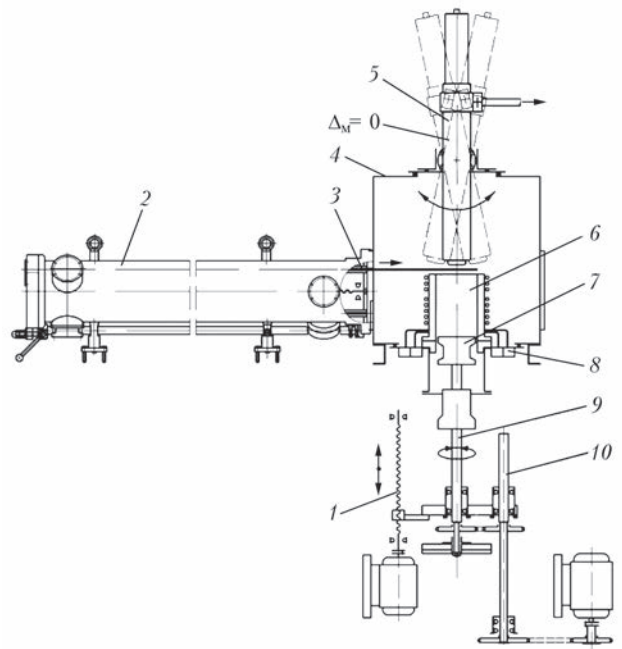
Принципова схема плазмово-індукційної установки УП-20 для вирощування монокристалів тугоплавких металів у формі тіл обертання: 1 — механізм вертикального переміщення монокристалу; 2 — бункер-касета для витратних прутків; 3 — витратний пруток; 4 — плавильна камера; 5 — плазмотрон; 6 — монокристал; 7 — піддон; 8 — водяний колектор; 9 — шток механізму вертикального переміщення монокристалу; 10 — механізм обертання монокристалу
